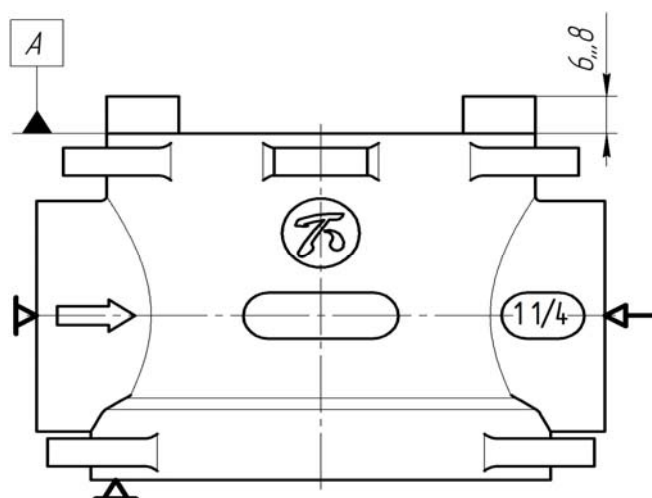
Эскиз корпуса, изготовленного на станке Daewoo Lynx 210A
